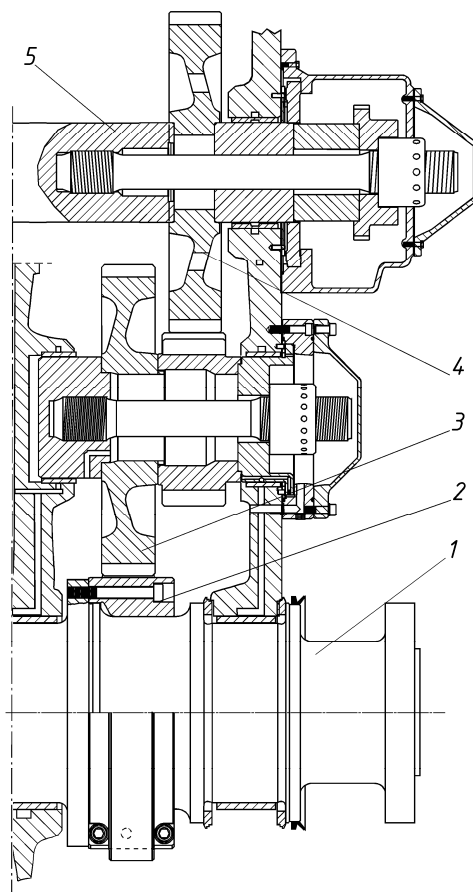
Шестерні приводу розподільного вала. 1 – колінчастий вал; 2 – ведуча шестерня; 3 – блок проміжних шестерень; 4 – відома шестерня розподільного вала; 5 – розподільний вал
